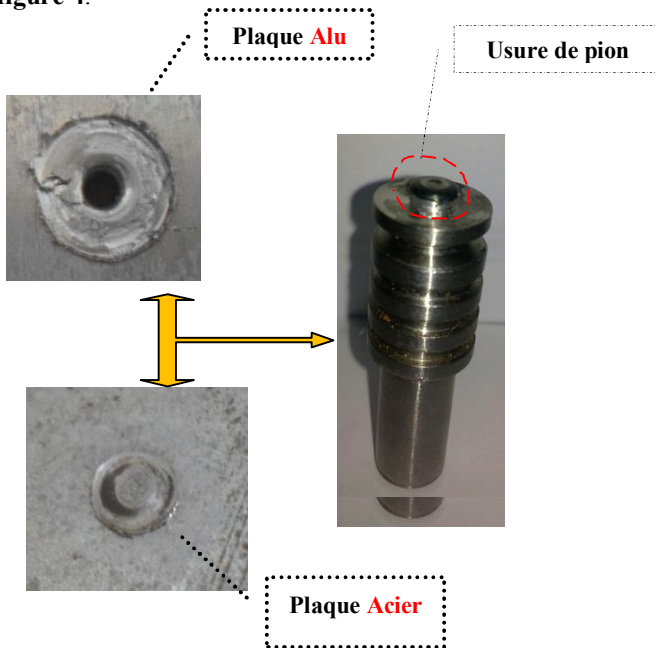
représentation de la soudure réalisée avec l'outil 1
